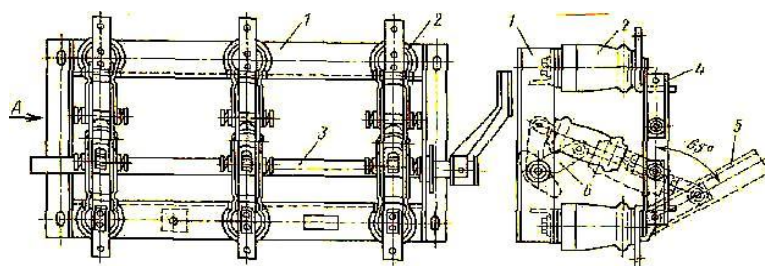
Трехполюсный разъединитель 1- рама; 2 - опорные изоляторы (при включенном положении); 3 - вал, 4 - неподвижный контакт, 5- контактный нож, 6- тяга
